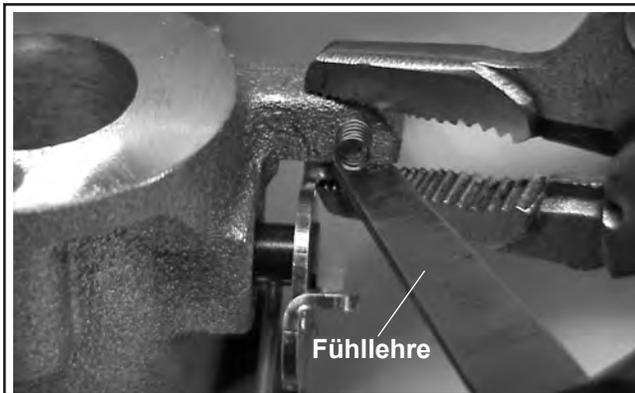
B-39. Einföhrung der Fühllehre (Motoren ohne Anschlagsschraube).
